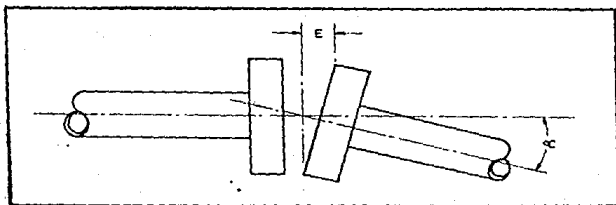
DESALINEAMIENTO AXIAL (ANGULO α Y DIMENSION E).
